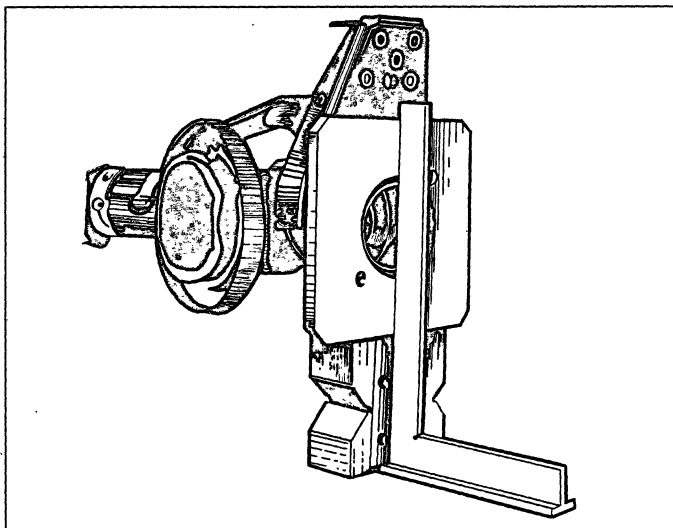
Проверка перпендикулярности поверхности крепления редуктора
